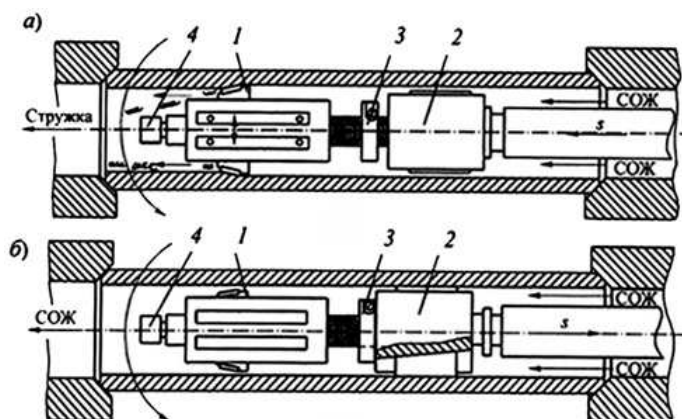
Комбинированный режуще-деформирующий инструмент фирмы «Sandvik Coromant»: а – растачивание; б – раскатывание
